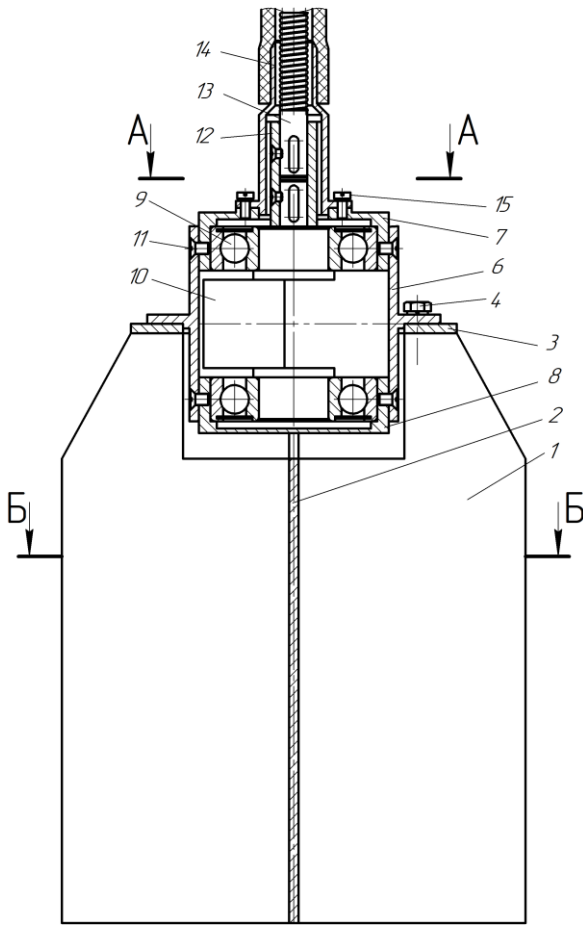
Общий вид крестообразного глубинного уплотнителя
